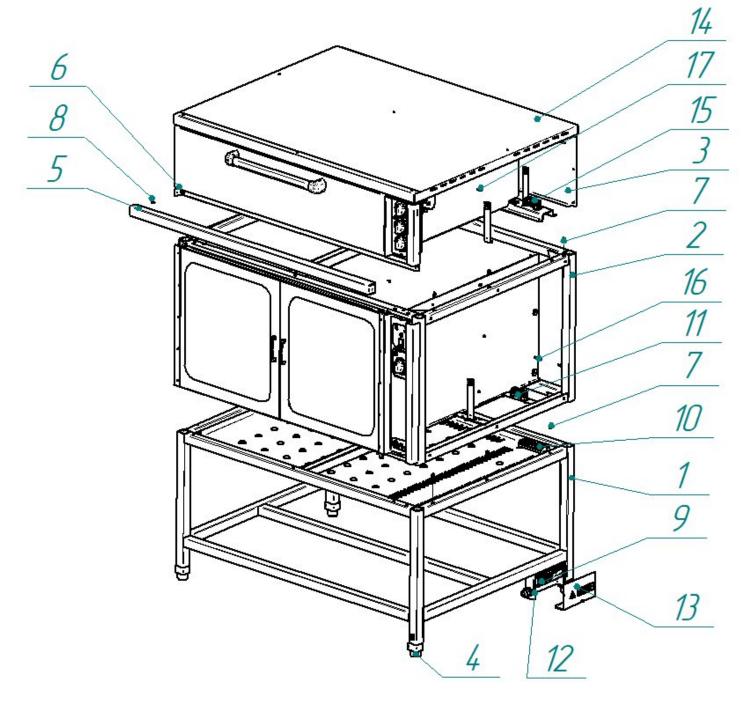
Схема сборки шкафа ШРТ 6-ЭШ + ЭШ-1К
